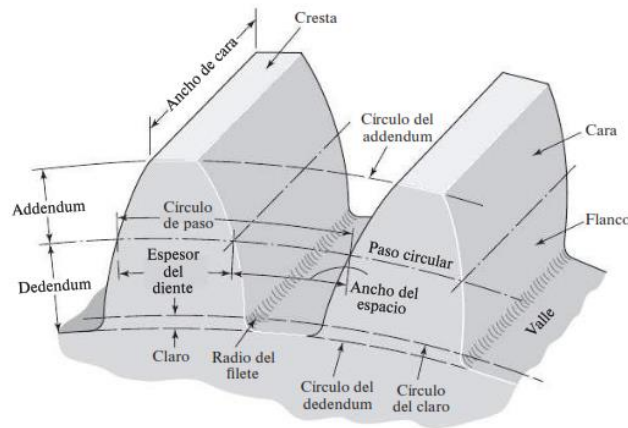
Nomenclatura de Engranajes cilíndricos rectos, perfil de involuta [12].
